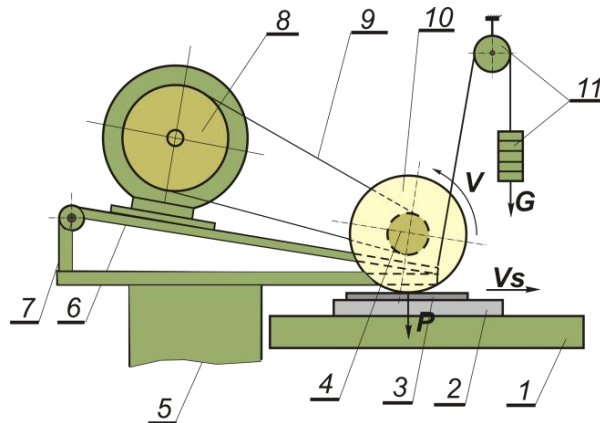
Принципова схема установки для зміцнювання високошвидкісним тертям
